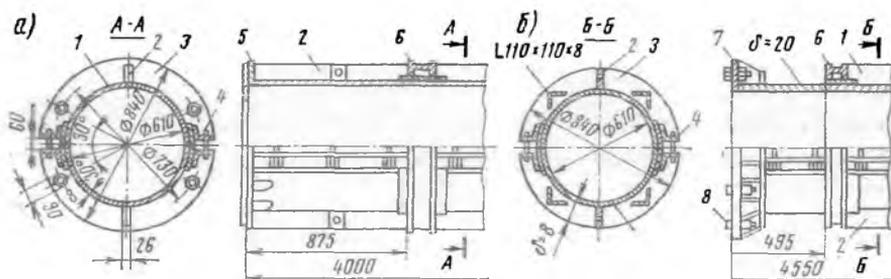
Формы для изготовления центрифугированных трубчатых свай: а — с ненапрягаемой арматурой; б — то же, с напрягаемой: 1 — обшивка; 2 — продольное ребро; 3 — поперечное ребро; 4 — откидной болт; 5 — фланец; 6 — бандаж; 7 — опорное кольцо; 8 — выдвижной выкат
